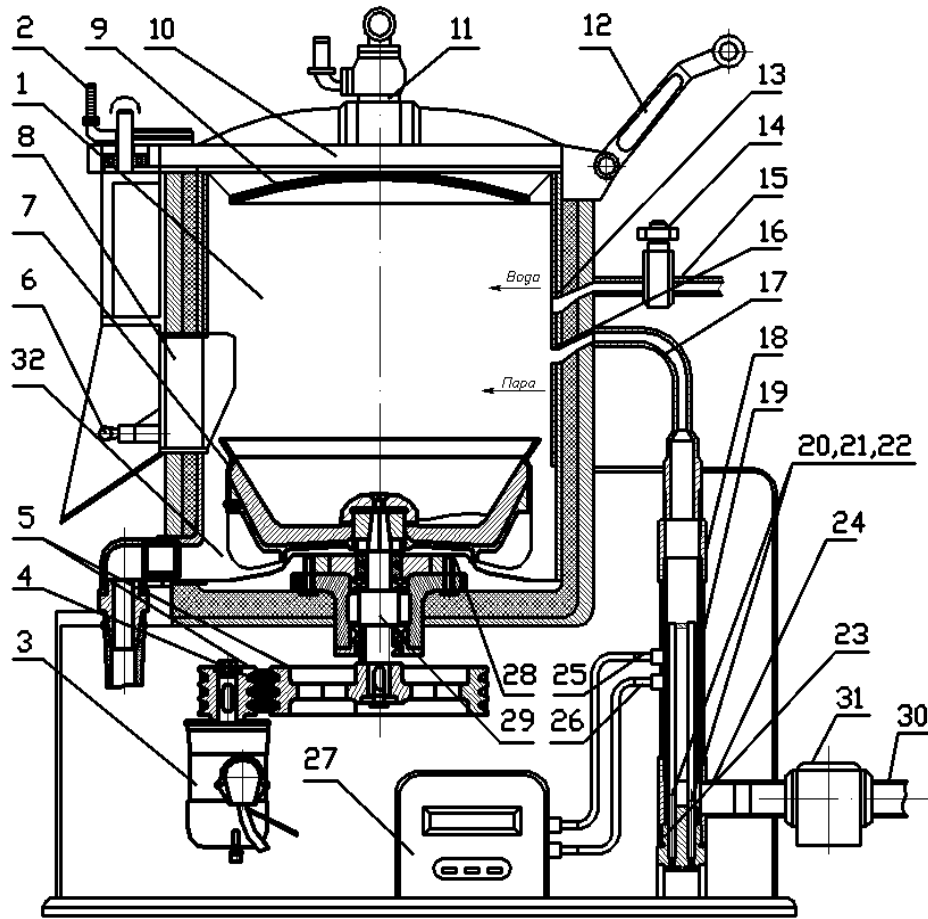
Схема промислового зразка апарата для комбінованого очищення бульбоплодів АКОБ: 1 – робоча камера апарата; 2 – ексцентриковий важіль; 3 – електродвигун; 4 – ремені; 5 – шків; 6 – ручка дверцят робочої камери; 7 – конусоподібна чаша; 8 – дверцята робочої камери; 9 – відбивач; 10 – кришка робочої камери; 11 – пристрій випуску пари; 12 – важіль кришки робочої камери; 13 – форсунка подачі води; 14 – кран подачі води; 15 – патрубок подачі води; 16 – форсунка подачі пари; 17 – патрубок подачі пари; 18 – вихідний патрубок парогенератора; 19 – парогенератор; 20, 21, 22 – електроди; 23 – блок фазних електродів; 24 – вхідний патрубок; 25 – нульовий контакт; 26 – заземлюючий контакт; 27 – панель управління парогенератором; 28 – лопаті; 29 – вал; 30 – патрубок подачі води до парогенератора; 31 – фільтр для очищення води; 32 – патрубок
